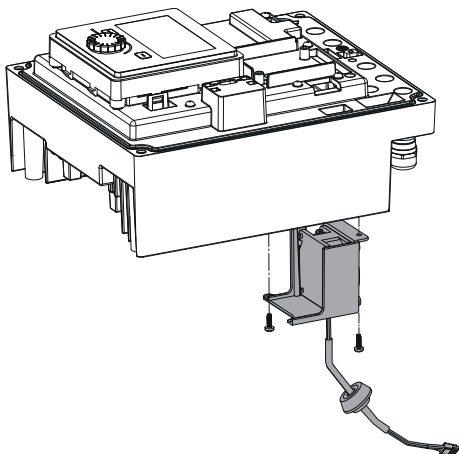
Retirar o ventilador do módulo, incluindo o cabo e o vedante de borracha
